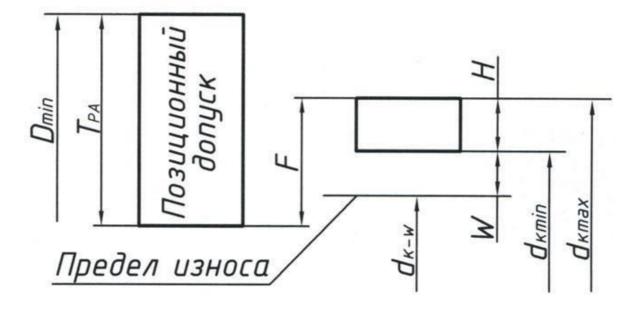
Поля допусков калибров для контроля отверстий при отсутствии базового элемента
